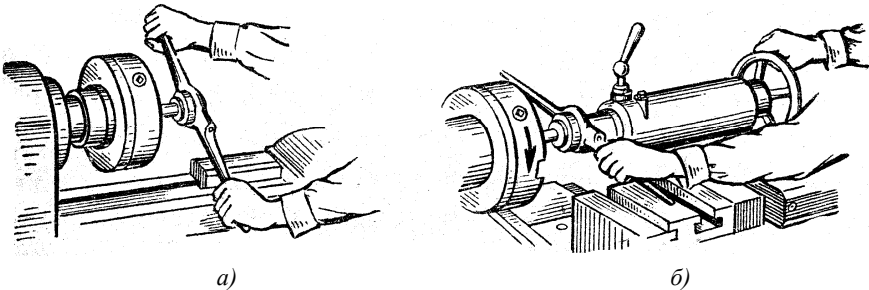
Нарізання різьби плашкою на токарному верстаті:
